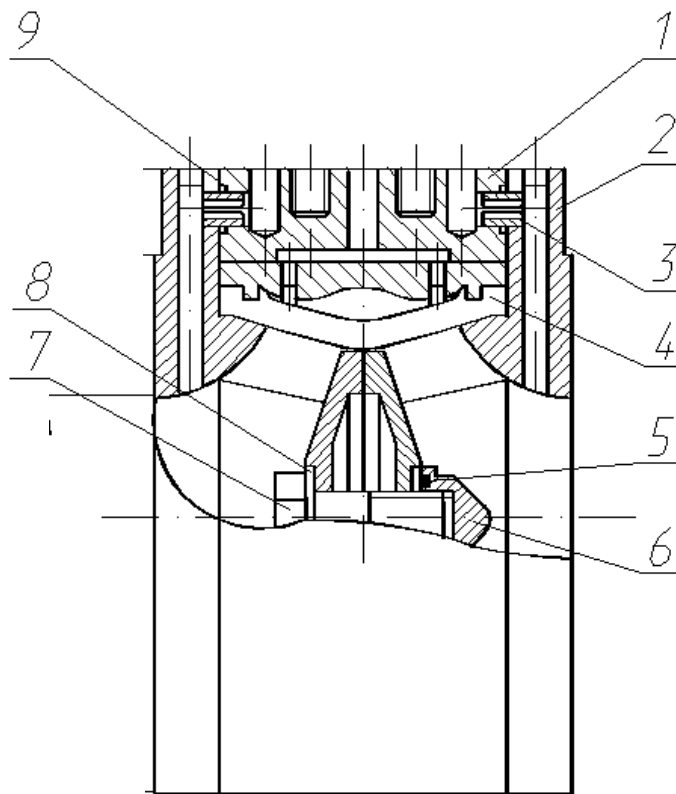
Сборочный чертеж клапана КЭО-01
